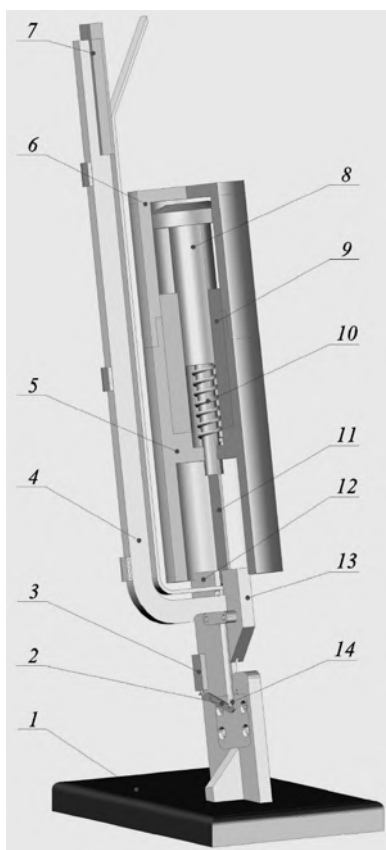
Клипсатор с дискретным ЛЭМД для наложения металлических скоб на упаковку запечатываемого продукта
